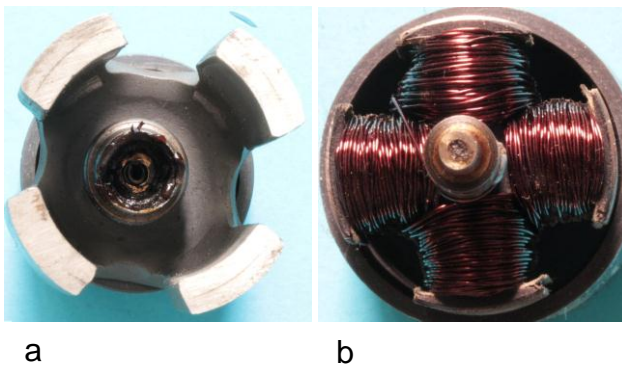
Baugruppen des Generators: a) Magnet mit Spurlager, b) Sternanker
